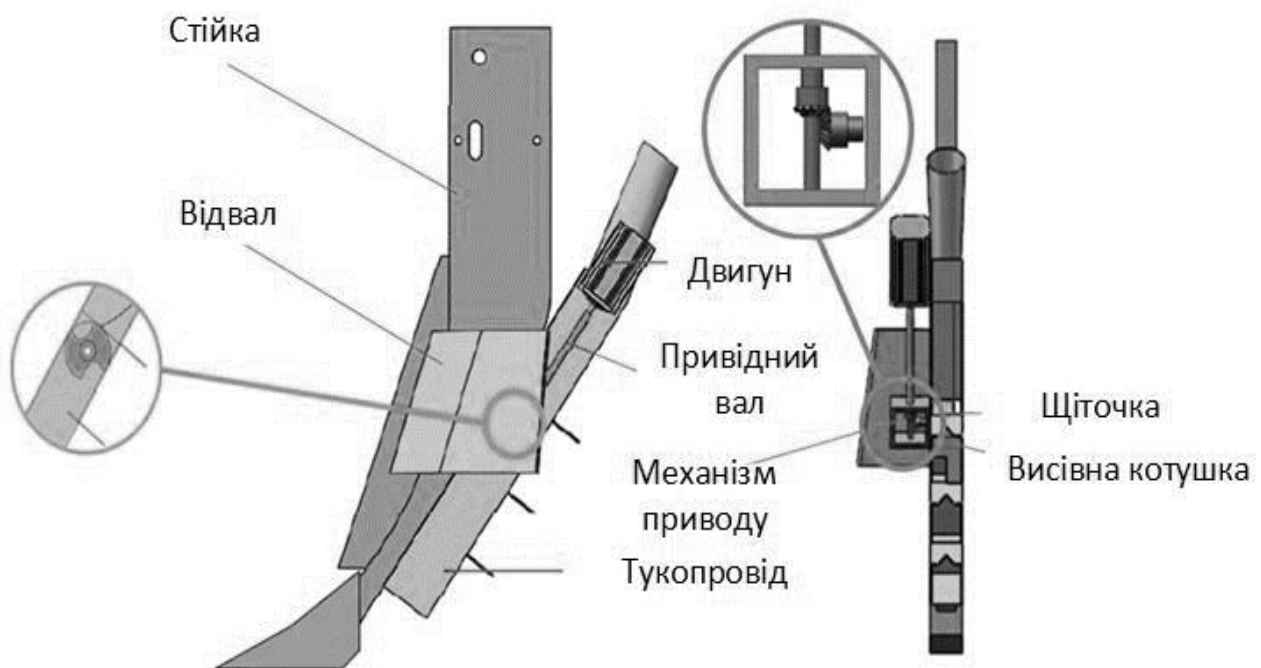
Конструктивні особливості сошника для глибокого внесення добрив
